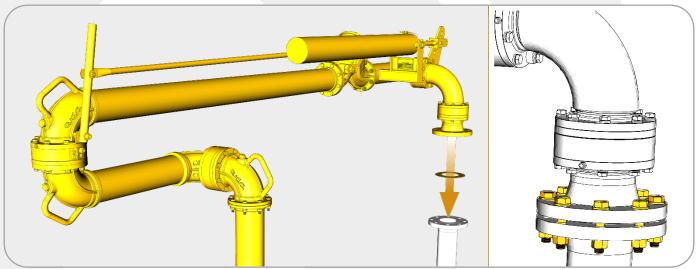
Fixação do Braço de Carregamento no Flange de Entrada
